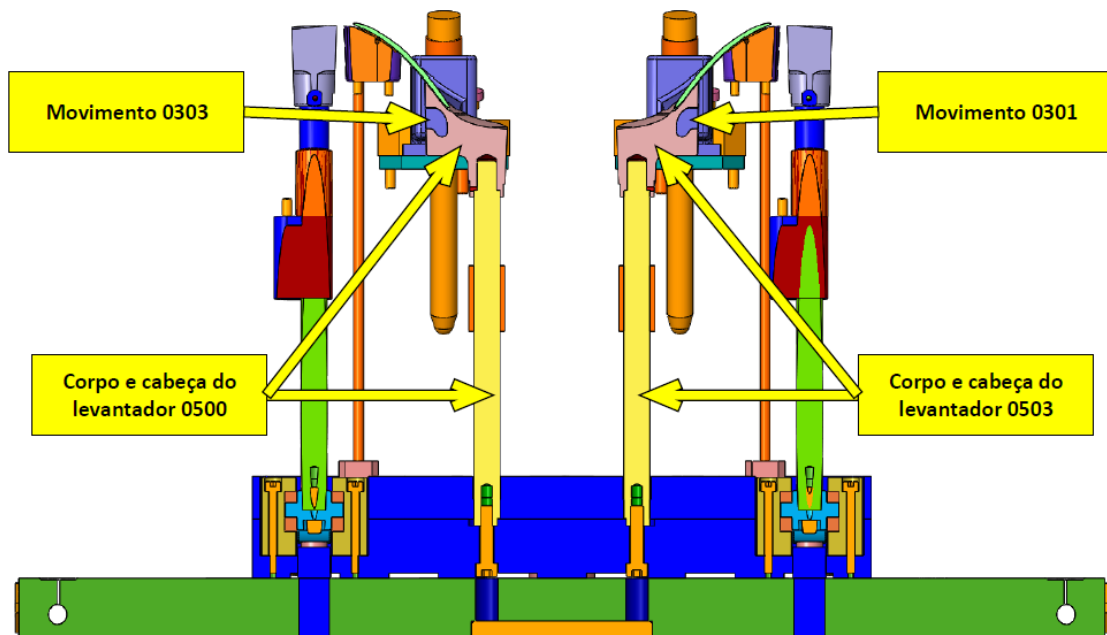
Vista em corte (lateral) dos levantadores verticais a 90°
